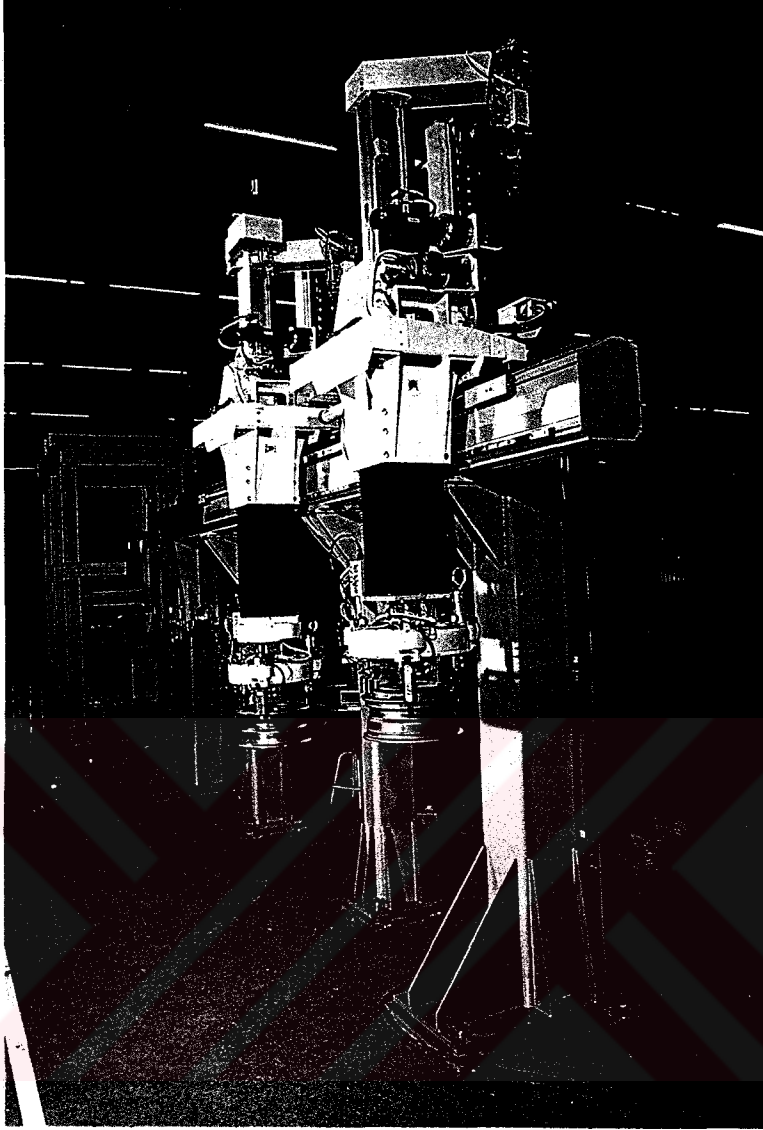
Renault 19 kaporta kaynak robotu. [9]
